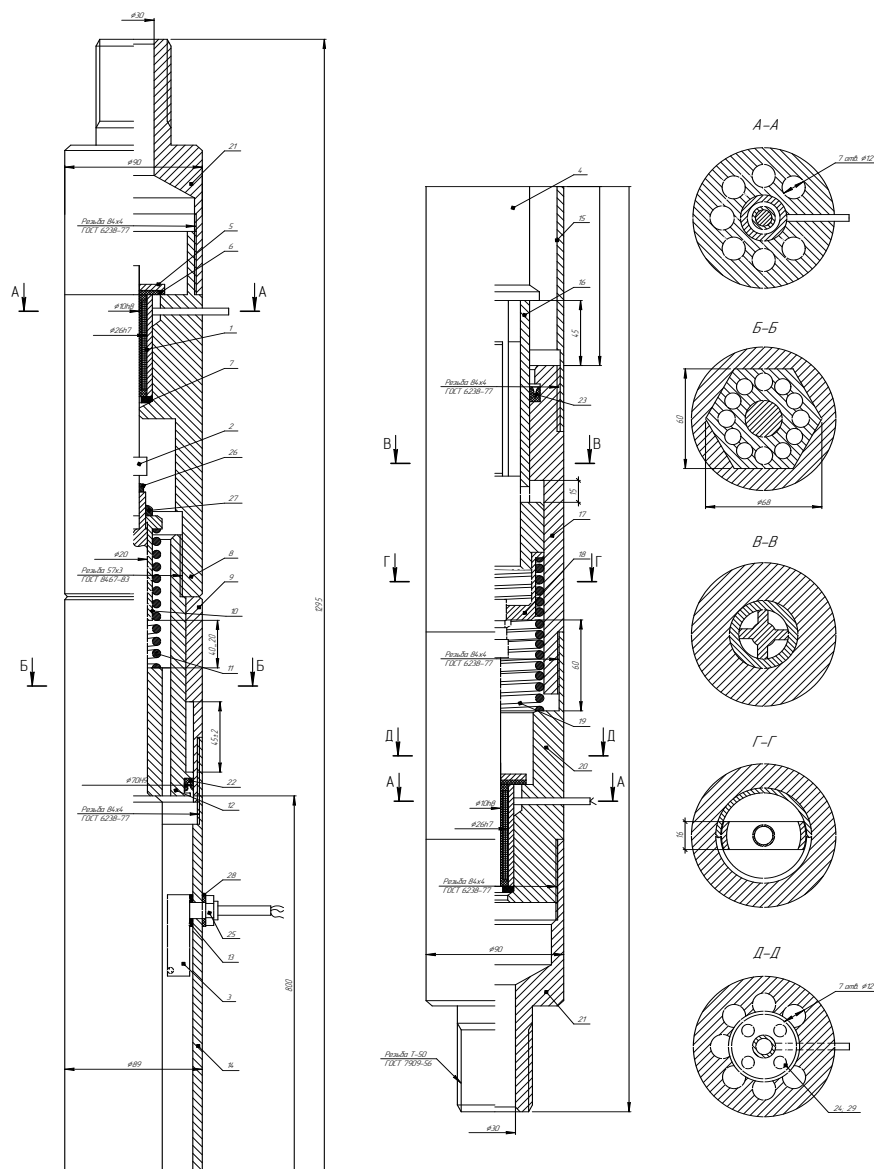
Схема экспериментального образца гидродинамического усилителя осевой нагрузки: 1 – датчик скорости; 2 – соединительная муфта; 3 – датчик давления; 4 – клапан; 5, 7 – шайбы упорные; 6 – прокладка; 8 – верхняя опора датчика скорости; 9 – шлицевой корпус; 10 – регулировочная гайка; 11 – пружина клапана; 12 – шлицевая втулка; 13 – уплотнительная шайба; 14 – корпус; 15 – рабочая камера; 16 – клапанная втулка; 17 – нижняя соединительная муфта; 18 – соединительный элемент; 19 – пружина клапанной втулки; 20 – нижняя опора датчика скорости; 21 – верхний (нижний) переходники; 22, 23 – уплотнения; 25, 26, 27 – стопорящие гайки.
